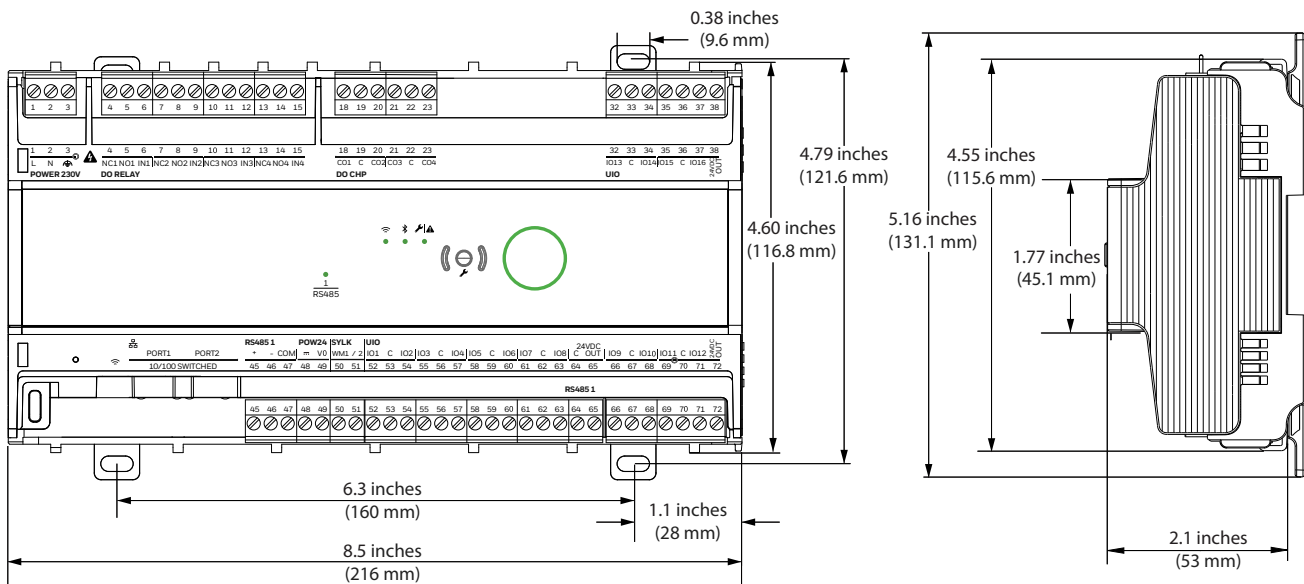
Abmessungen Regler mit Großes Gehäuse
